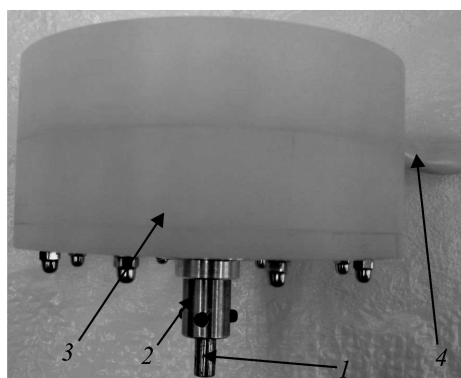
Внешний вид ЭУ для ЭДО: 1 – электрод; 2 – цанга; 3 – корпус; 4 – силовой кабель.
